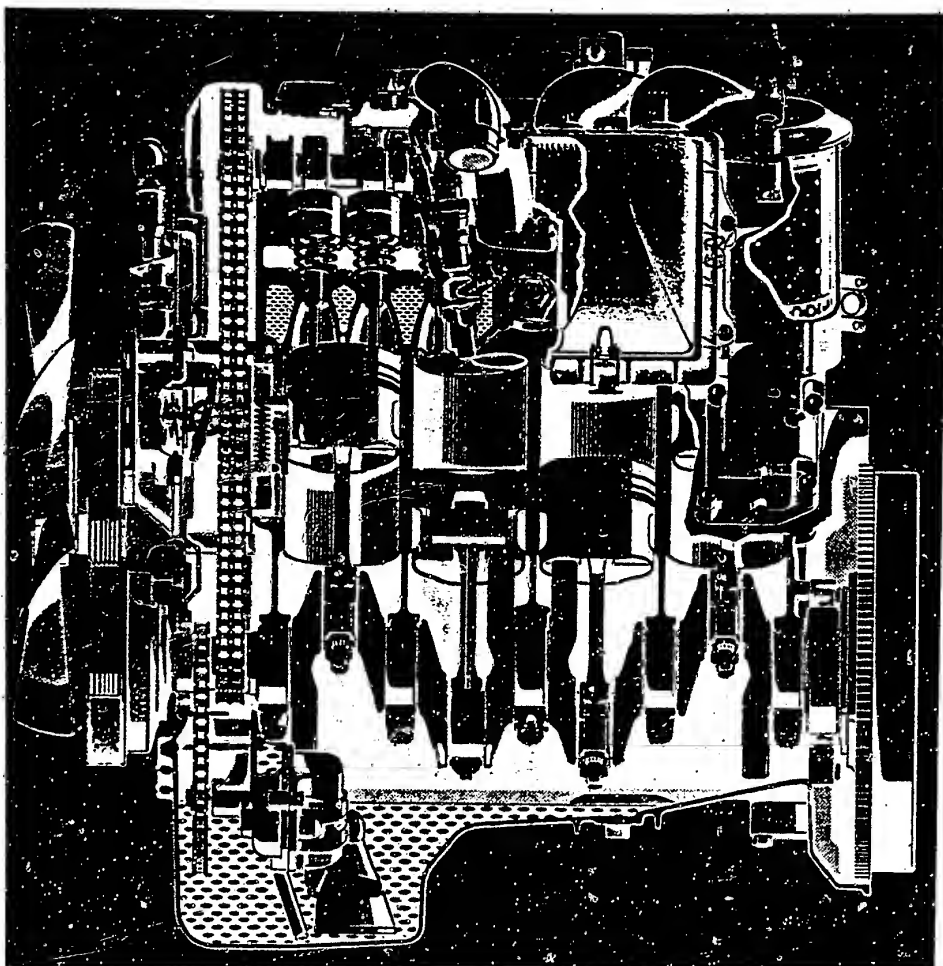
Dieselmotor 601.911: Längsschnitt durch den 4-Zylinder-Reihenmotor mit obenliegender Nockenwelle.
